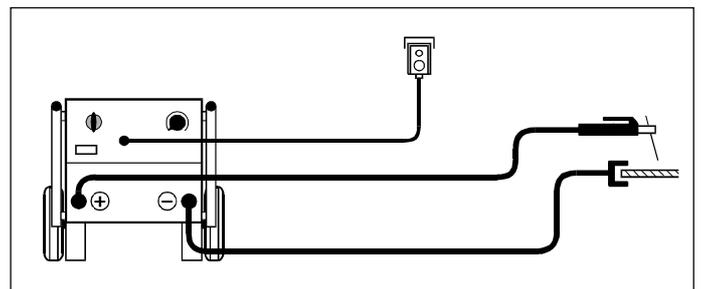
WTU en tant que source de courant du soudage manuel à l'électrode enrobée
